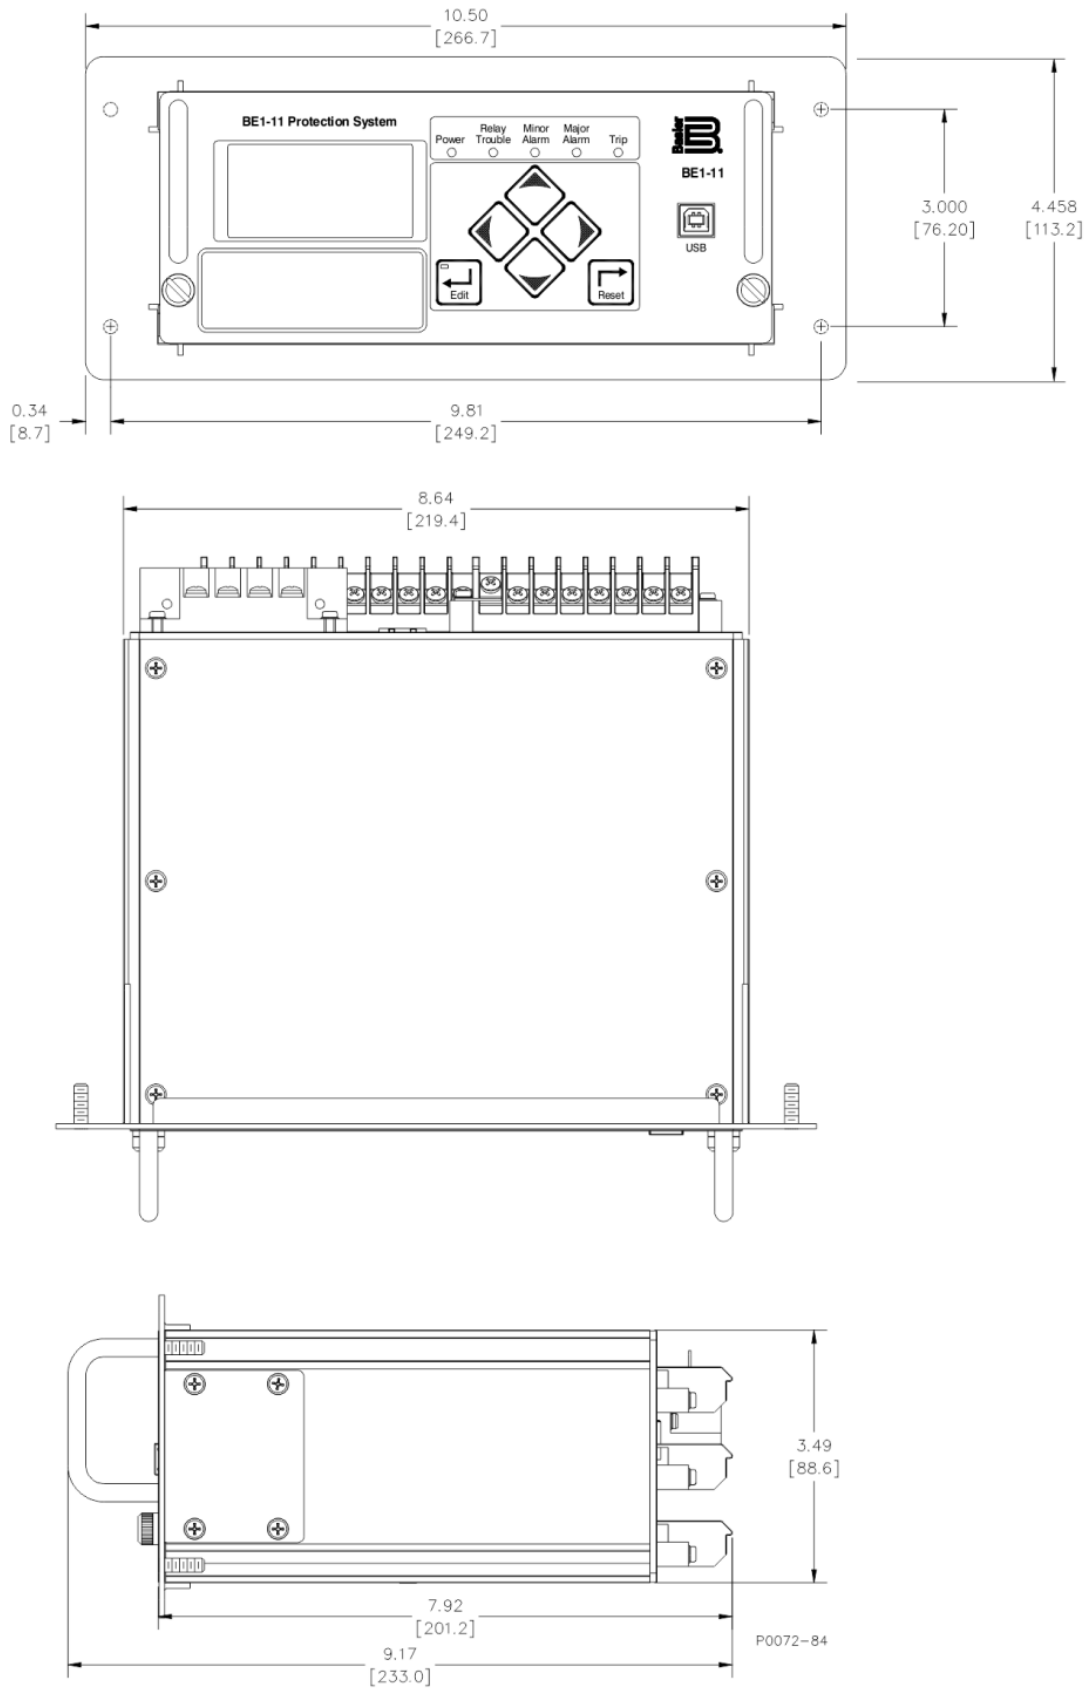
Dimensions du boîtier pour montage sur panneau H1
